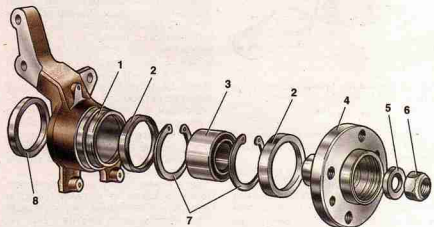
Поворотный кулак и детали ступицы переднего колеса: 1 — поворотный кулак; 2 — наружное грязезащитное кольцо; 3 — подшипник ступицы; 4 — ступица колеса; 5 — упорная шайба; 6 — гайка; 7 — стопорное кольцо; 8 — внутреннее грязезащитное кольцо
